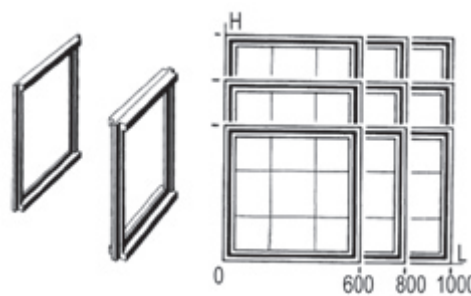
Общий вид литых рам и схема типоразмерного ряда
